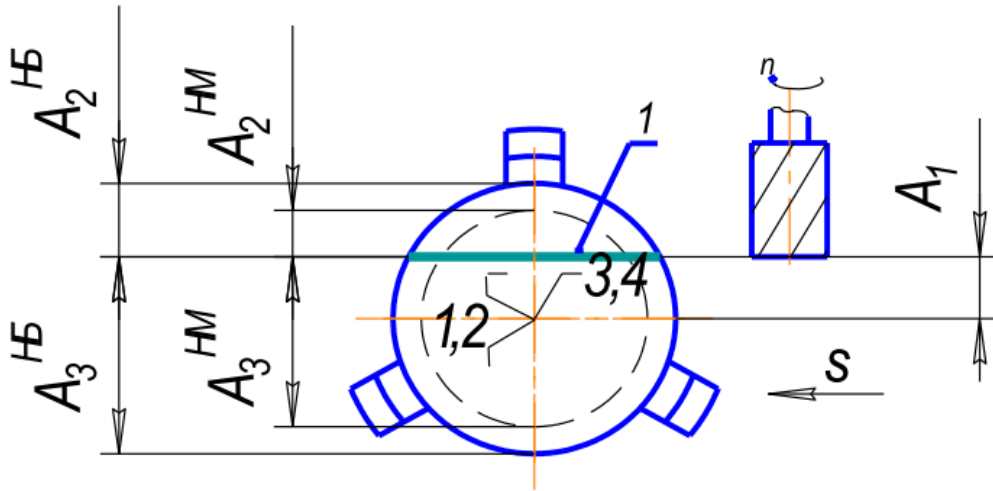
Схема установки валу в самоцентрувальний патрон
